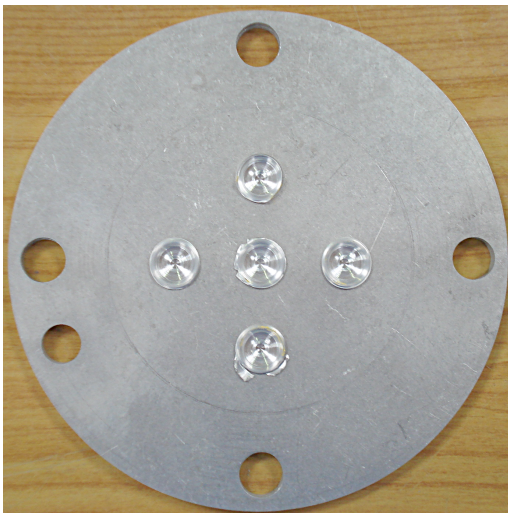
Plusieurs points de soudure sur une même éprouvette
